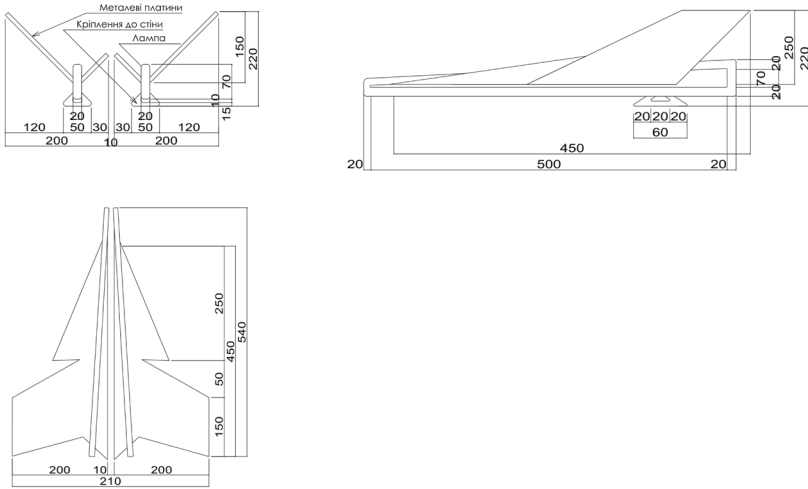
Схема освітлювального приладу у вигляді літака з габаритними розмірами
